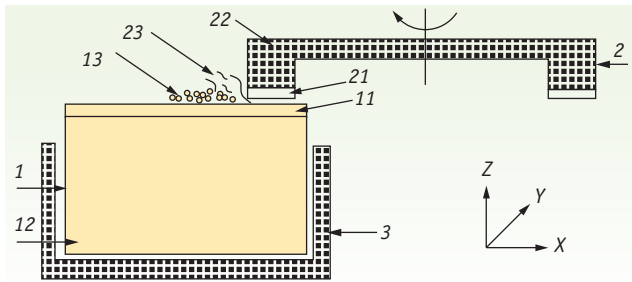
Система «инструмент – обрабатываемый материал»: 1 – образец; 11 – поверхностный слой образца; 12 – внутренний объем образца; 13 – пыль от обработки образца; 2 – шлифовальный круг; 21 – поверхностный слой шлифовального круга; 22 – внутренний объем шлифовального круга; 23 – пыль от шлифовального круга; 3 – державка
